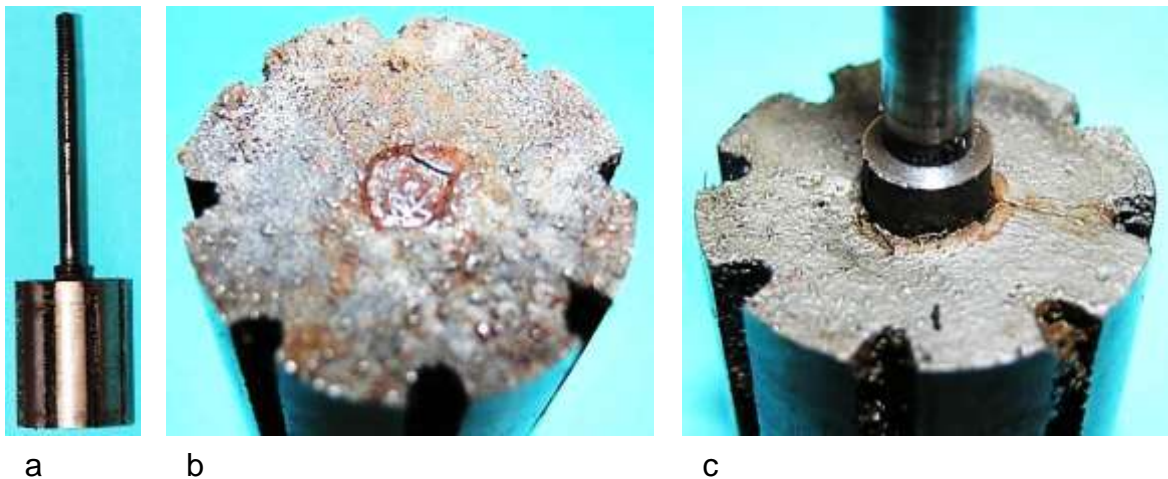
Polrad: Durchmesser: 21,5 mm, Länge: 28 mm, Wellendurchmesser: 4 mm, a) Polrad mit Welle, b) Untere Stirnseite, c) Obere Stirnseite
